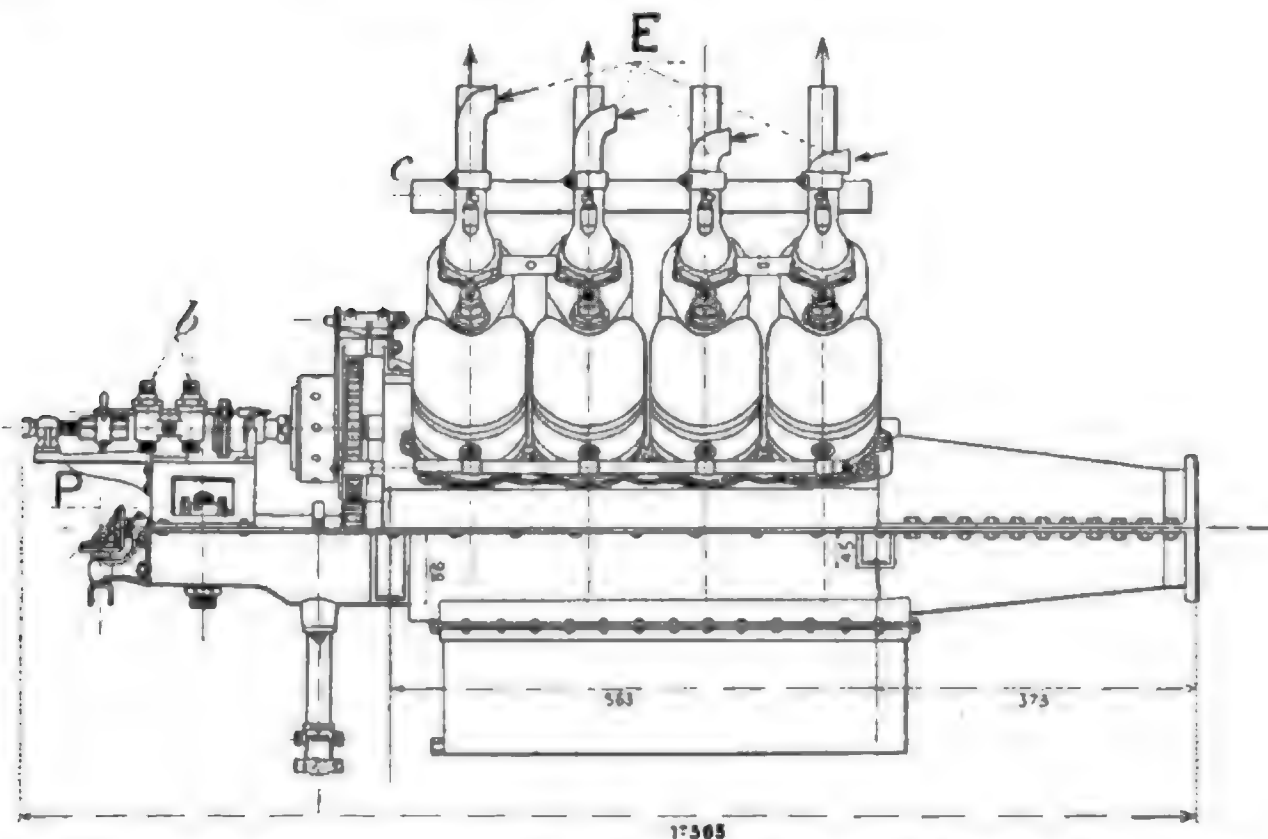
Zeichnung des Flugmotors 'Antoinette', Seitenansicht. *A* Auspuffrohre, *E* Einlaßrohre, *c* Wasserauslaß, *b* Öl- und Benzinpumpe, *P* Wasserpumpe.
